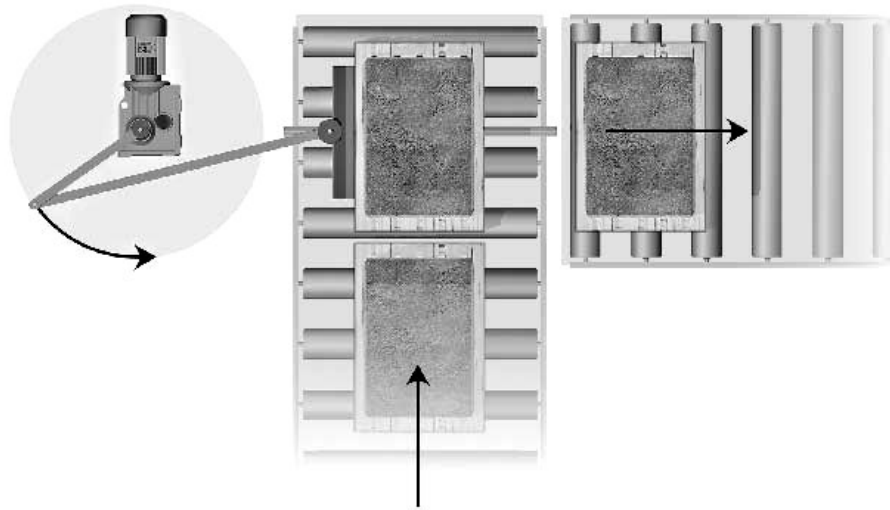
Передавальний пристрій із кривошипно-шатунним механізмом
